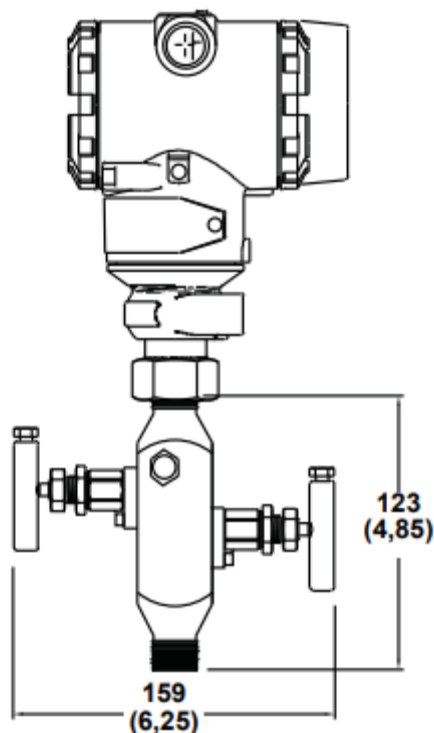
Преобразователь Rosemount 3051CG в сборе с клапанным блоком
